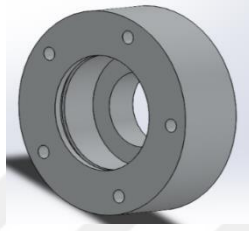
9. Mil 3D Solidworks tasarım çizimi
